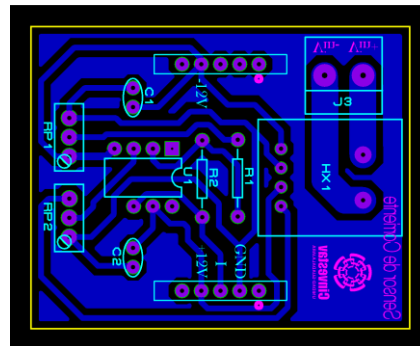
Sensor de corriente en PCB Di. Pr.
